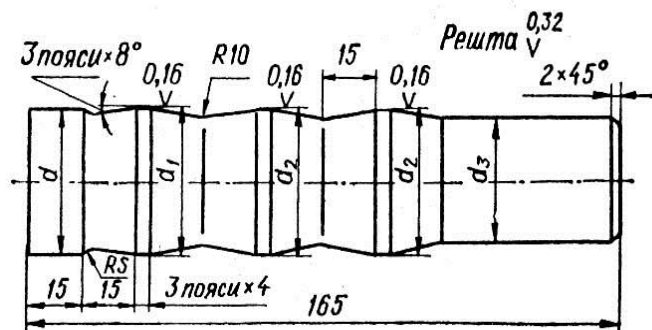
Дорн для калібрування запресованої і розточеної втулки верхньої головки шатуна двигуна ЗМЗ-53:
